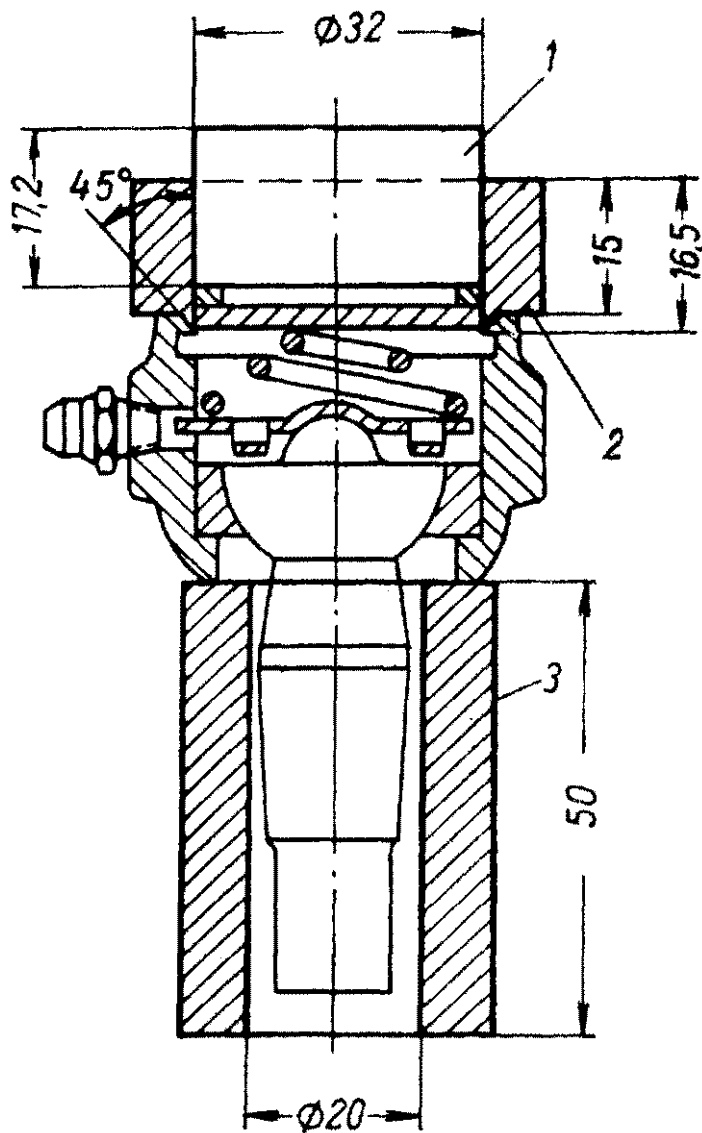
Приспособление для сборки шарнира рулевых тяг:
